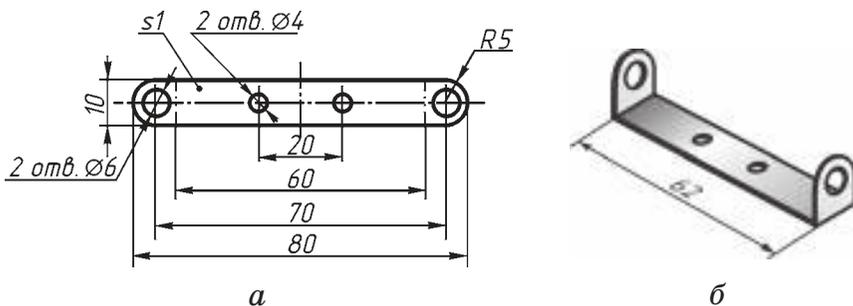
Чертёж (а) и технический рисунок (б) скобы крепления оси
